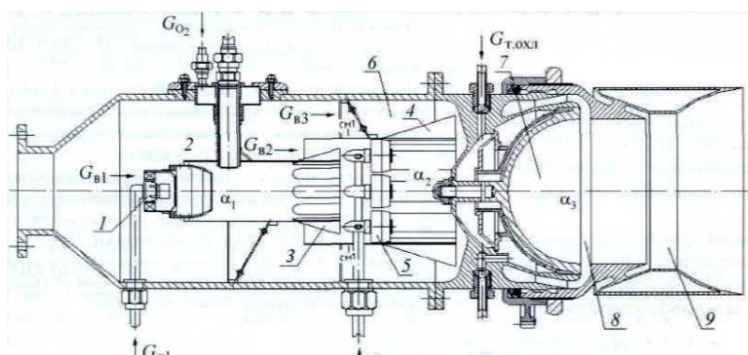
Конструктивная схема ТМ ПудФК с ЭУТ: 1 - форсунка для запуска реактора и подогрева воздуха в нем; 2 - пусковое устройство; 3, 4 - смеситель; 5 - основные форсунки; 6 - реактор; 7 - резонатор; 8 - кольцевое сопло; 9 - эжекторный усилитель тяги (ЭУТ)
